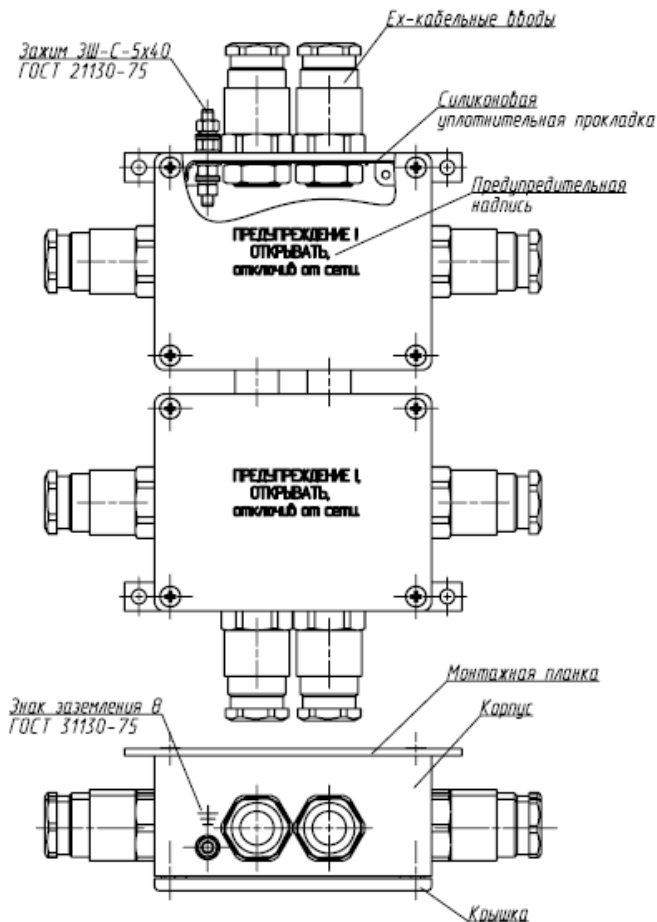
Блок корпусов и коробка клеммная ЕхБКО- А13В1/А55А2В2/А13А3 (скрепление корпусов типоразмеров 13, 55 и 13 сторонами В1-А2, В2-А3) – вариант 12
